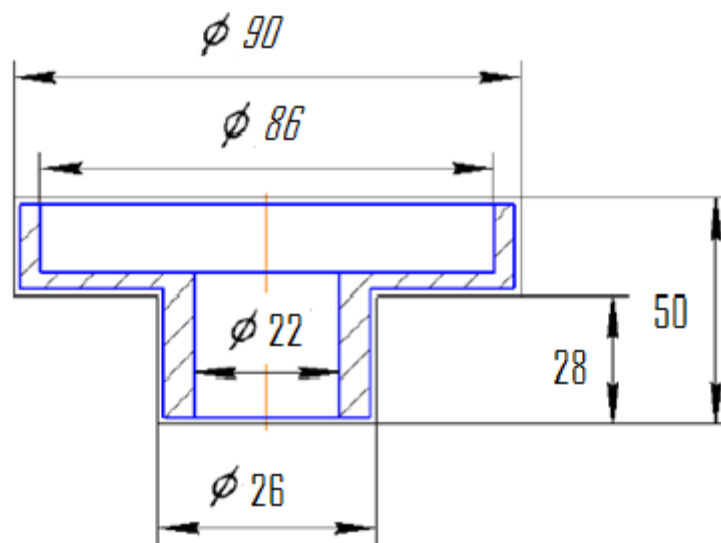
Заготовка деталі «Напівмуфта»
